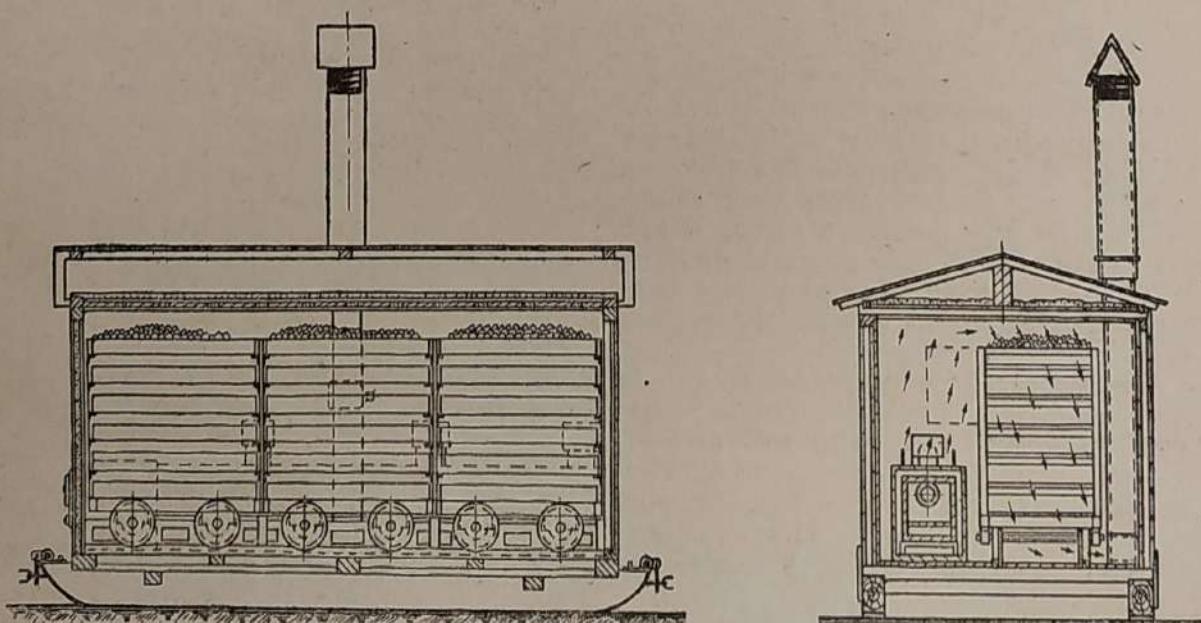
Передвижная сушилка ЦНИИМЭ 2П,
